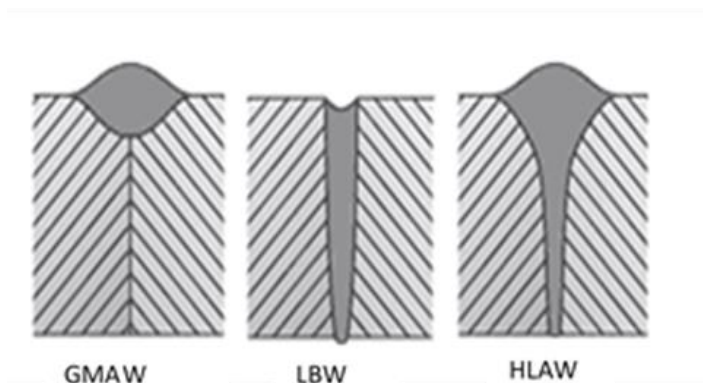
Diferencias de penetración de soldadura [22].
